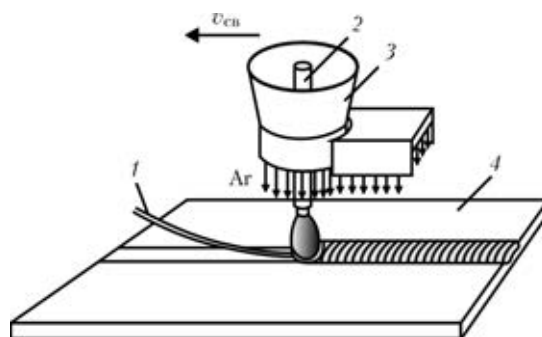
Схема процесса дуговой сварки титана вольфрамовым электродом: 1 — присадочная проволока; 2 — вольфрамовый электрод; 3 — защитное сопло; 4 — наплавляемое изделие
